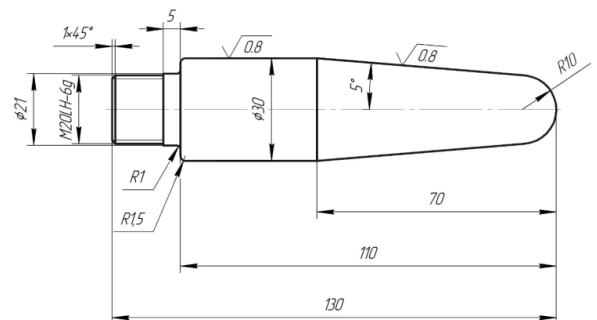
Оправка для прошивки заготовок диаметром 65 мм
